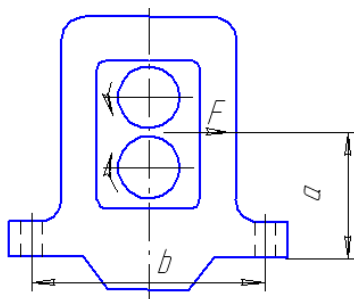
К расчёту рабочей клетки на опрокидывание
